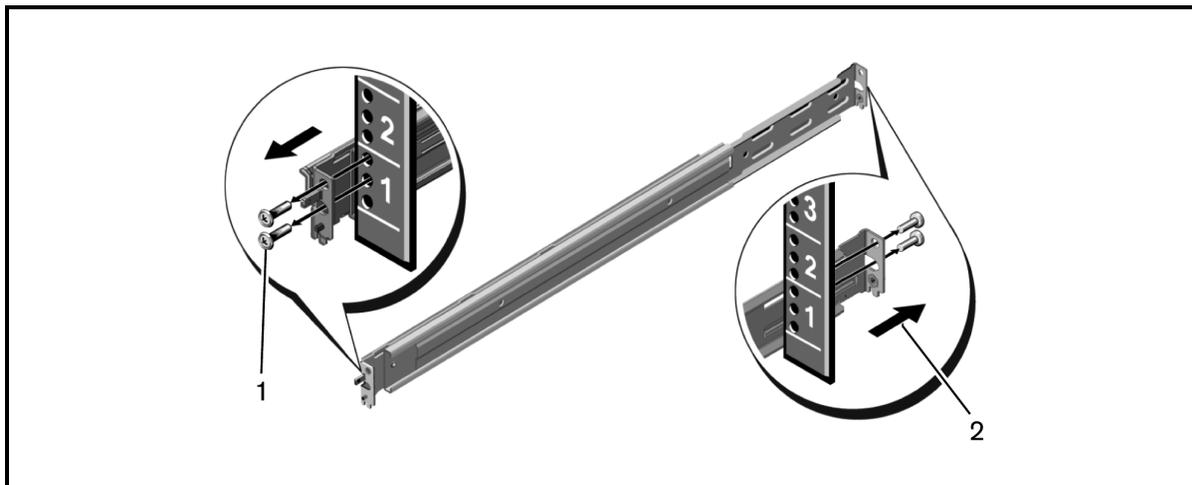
Entfernen der Schienen ohne Werkzeuge
